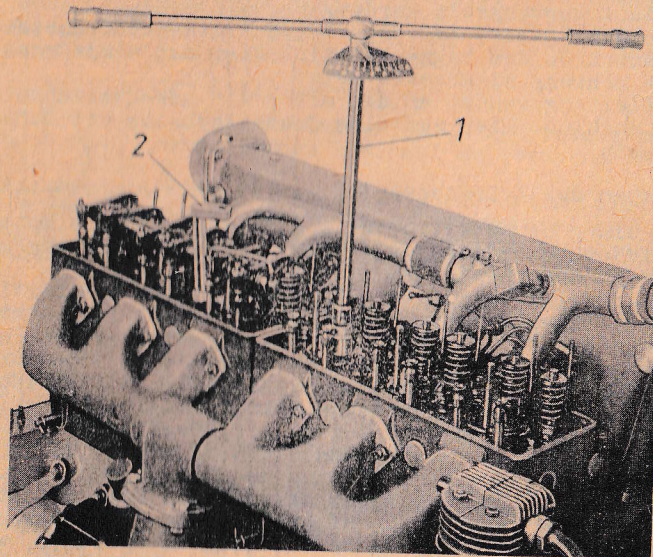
Anziehen der Muttern zur Befestigung des Zylinderkopfes
